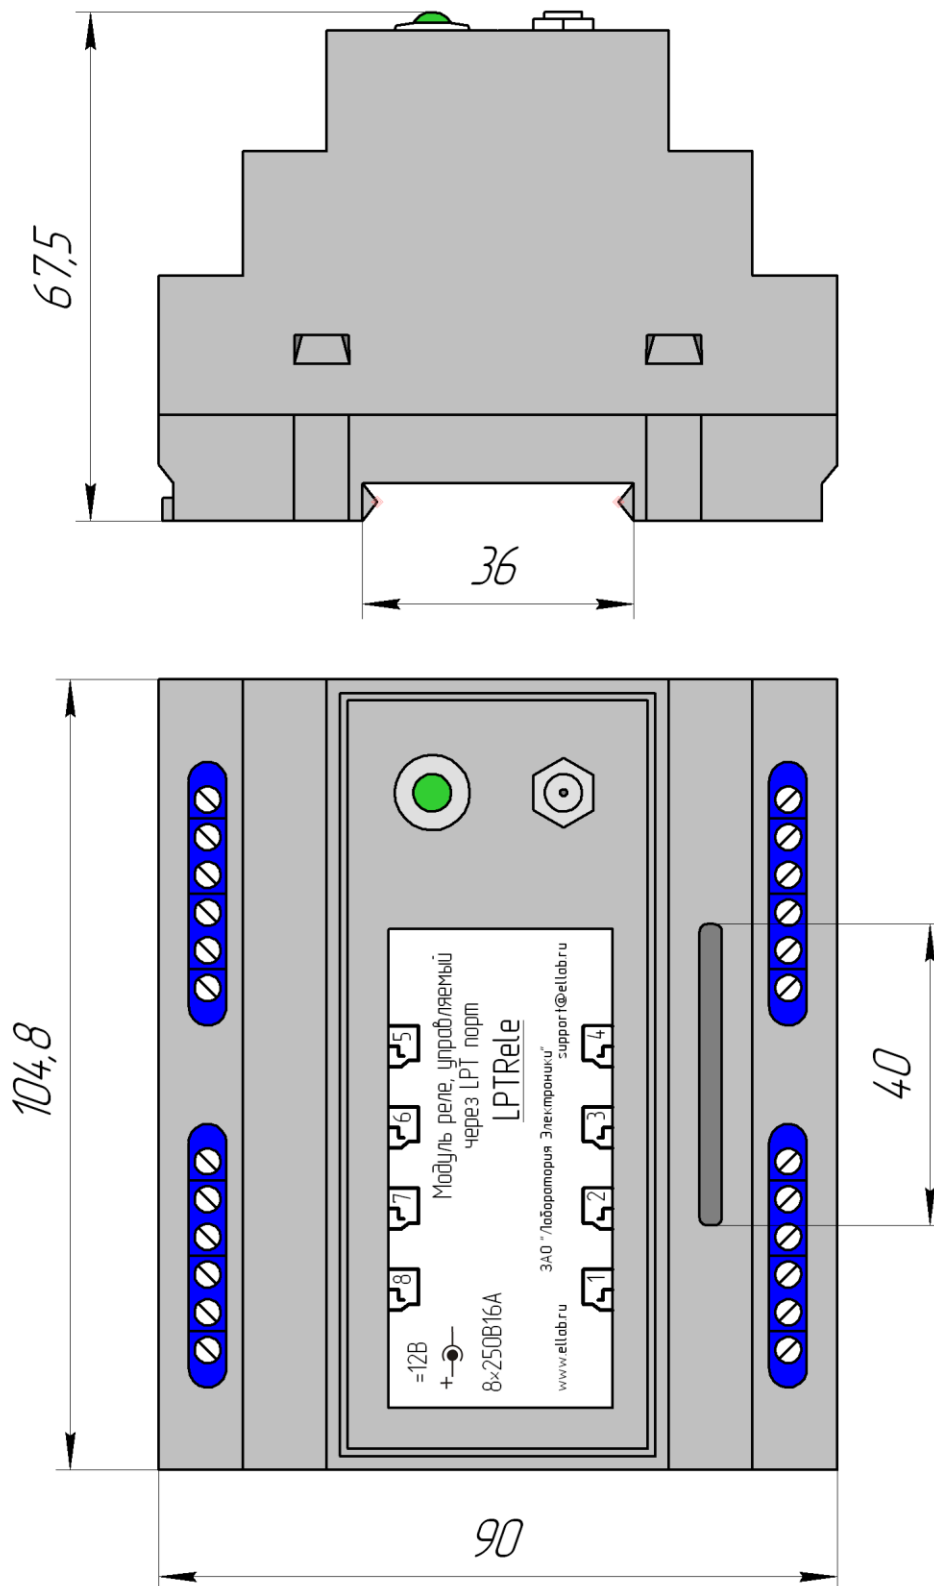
Габаритные и установочные размеры блока управления в корпусе
